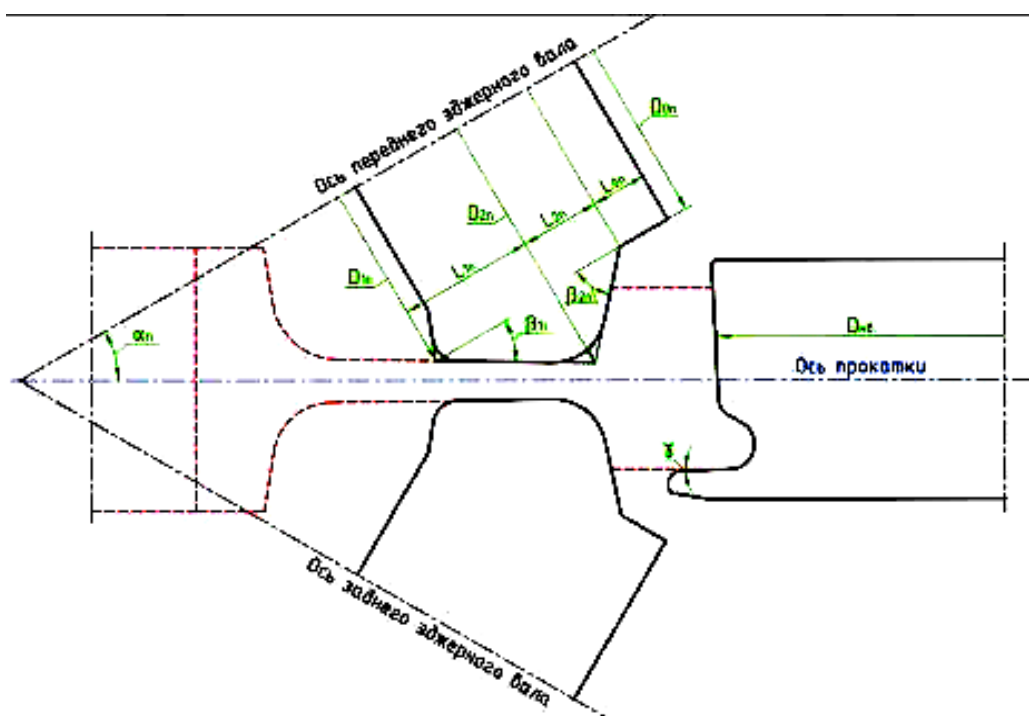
Положение эджерных и нажимного валков при прокатке заготовки колеса на колесопрокатном стане
